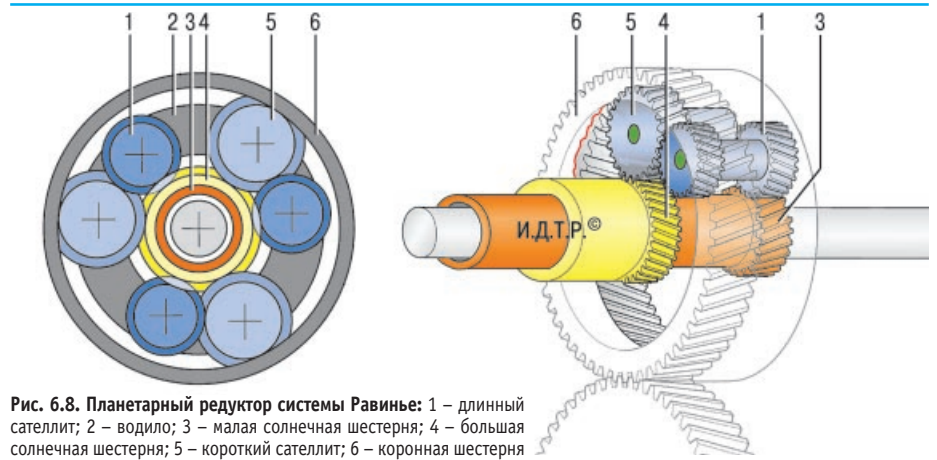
Планетарный редуктор системы Равинье: 1 – длинный сателлит; 2 – водило; 3 – малая солнечная шестерня; 4 – большая солнечная шестерня; 5 – короткий сателлит; 6 – коронная шестерня
